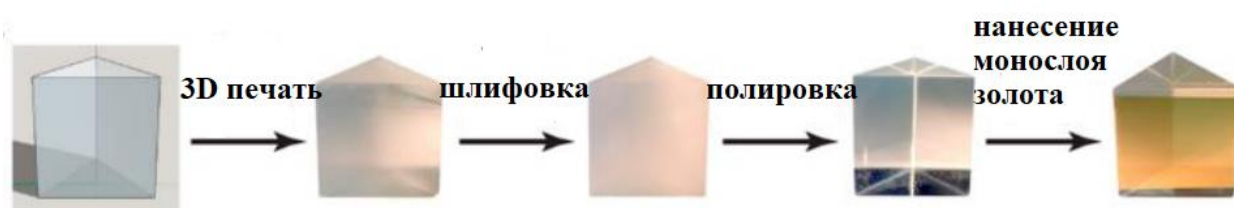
Схема изготовления 3D напечатанных поверхностных плазмонных устройств [22]
